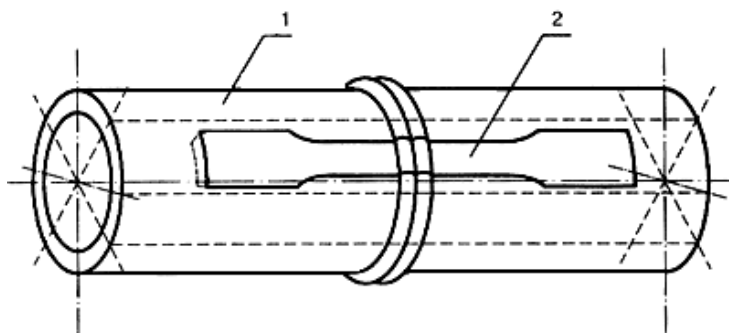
Схема вырезки образцов из сварного соединения для испытания на осевое растяжение
